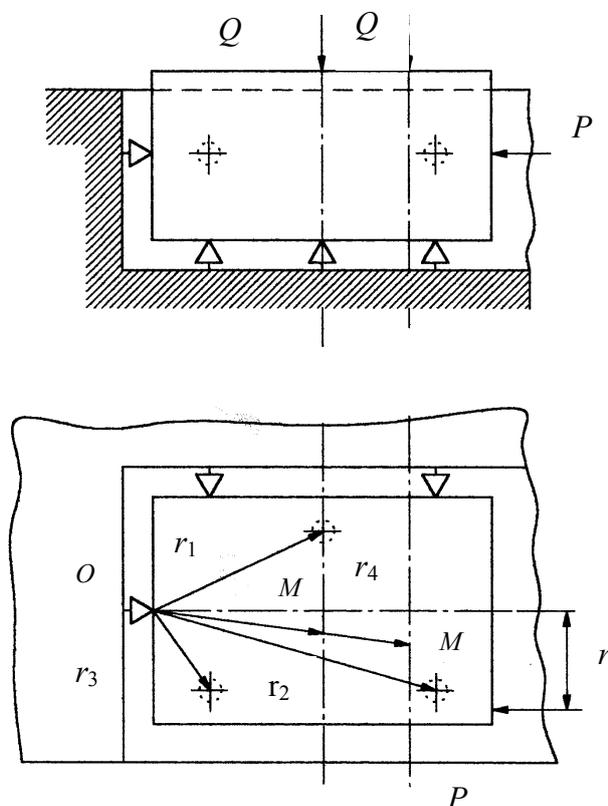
Схема для расчета зажимного устройства предотвращающего поворот заготовки
